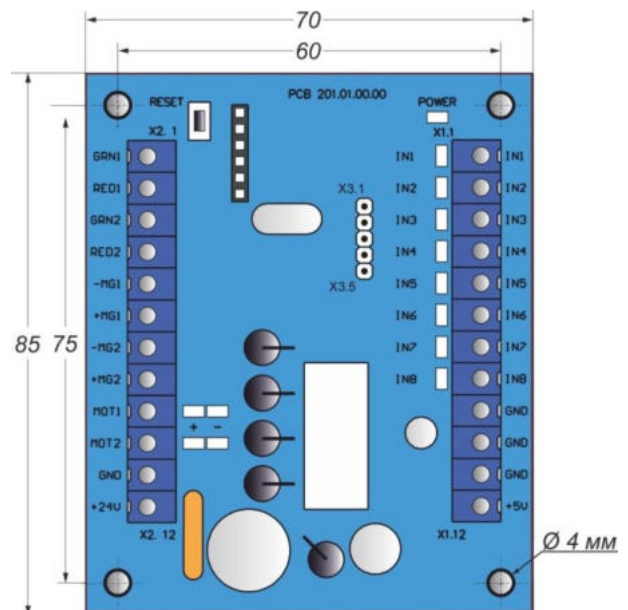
Зовнішній вигляд, габаритні та приспонувальні розміри контролера PCB.201.01.00.00
